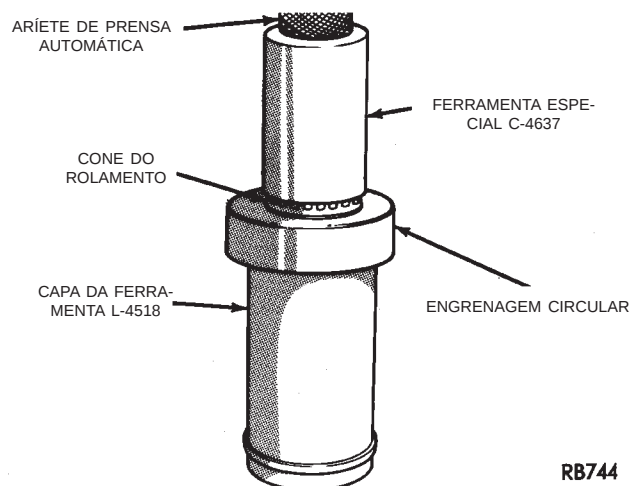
Instalação do Cone de Rolamento da Engrenagem Circular Traseira com Dentes Interiores
